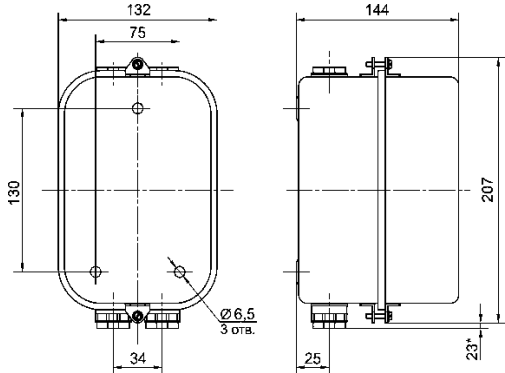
Пускатель ПМ12-025 25А в защитном корпусе - IP40; IP54
